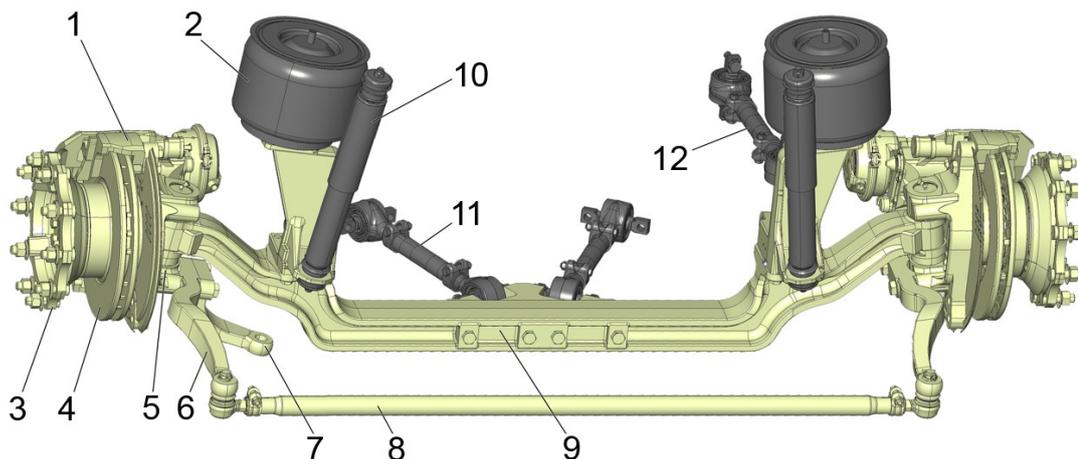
Передняя ось с реактивными штангами, амортизаторами и пневмобаллонами подвески:
